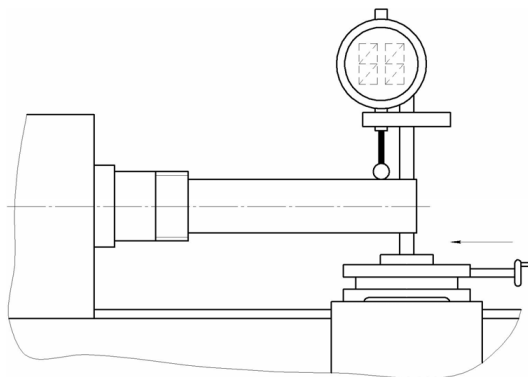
Схема установки индикатора для проверки параллельности направления перемещения салазок суппорта относительно оси шпинделя
